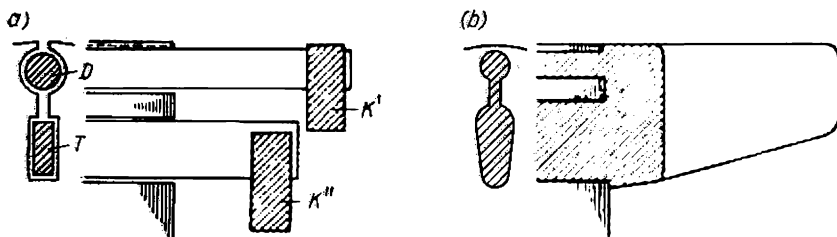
Rotor d'un moteur à deux cages: a) à deux enroulements, b) rempli d'aluminium.
